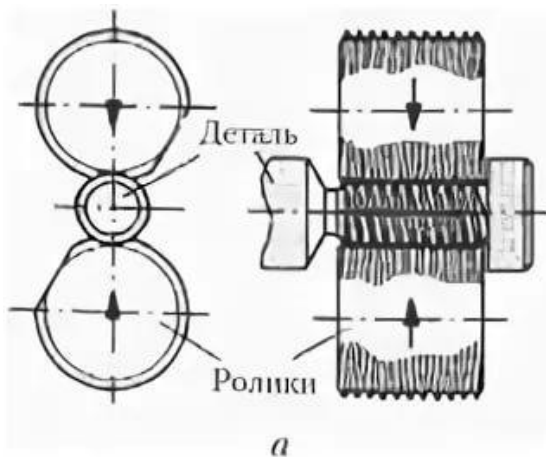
Резьбонакатная плашка: схема и конструкция
